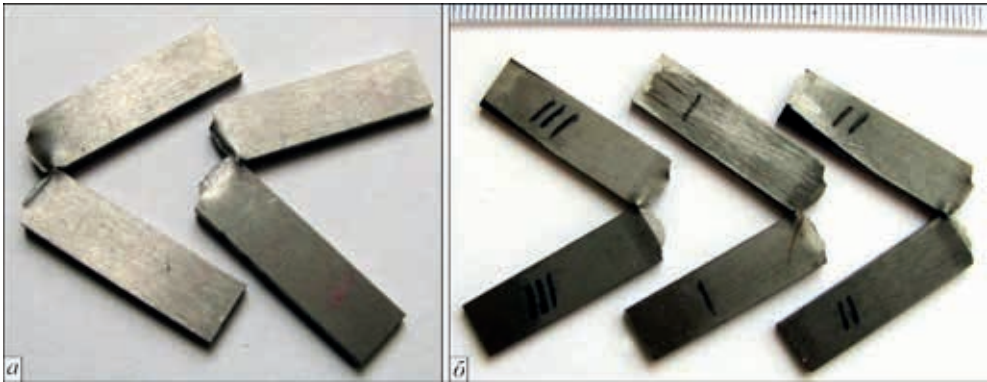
Зовнішній вигляд зруйнованих зразків: а – основний метал; б – зварне з'єднання
